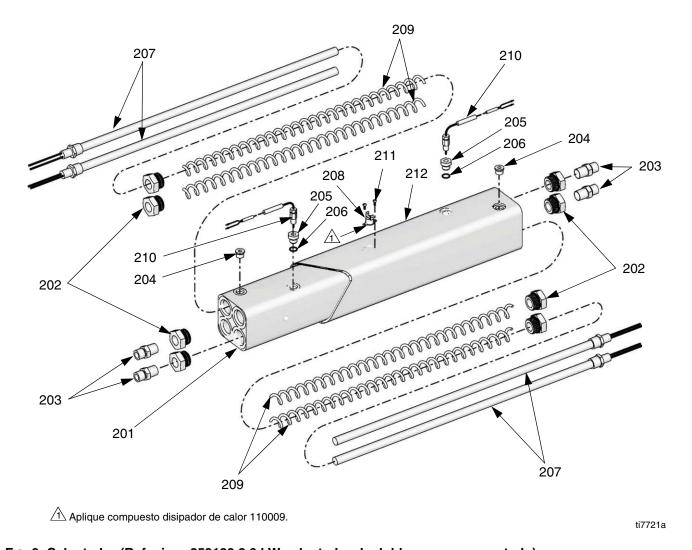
Calentador (Ref. pieza 253189 8,0 kW calentador de doble zona representado)
